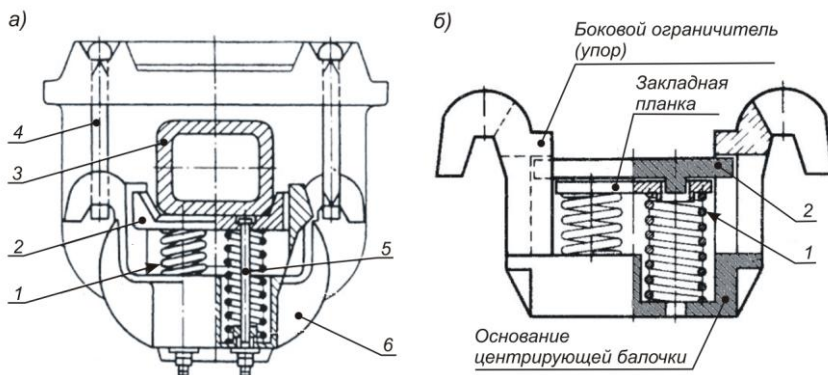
Центрирующие приборы с упругой опорой хвостовика грузового вагона болтовой (*а*) и безболтовой (*б*) конструкции:
